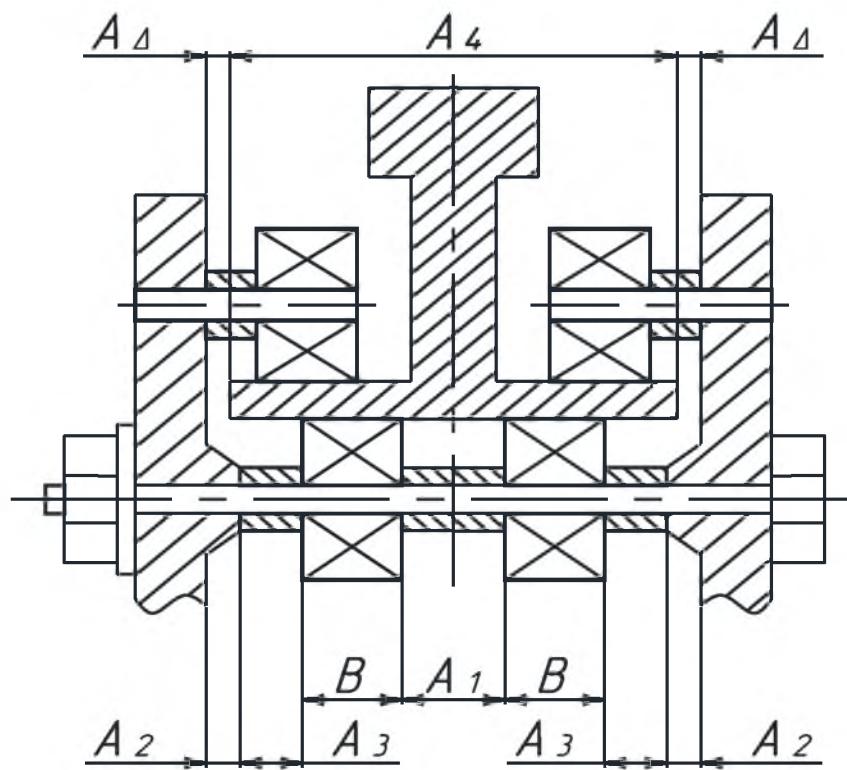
Эскиз крепления каретки выдвижного закрылка к лонжерону
